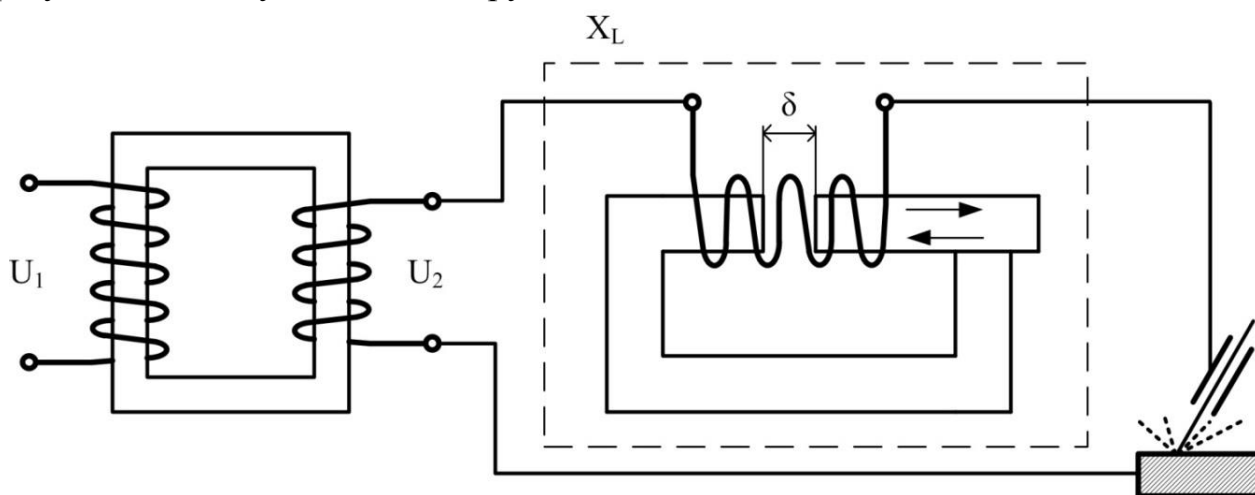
Схема вмикання зварювального трансформатора типу СТЕ
